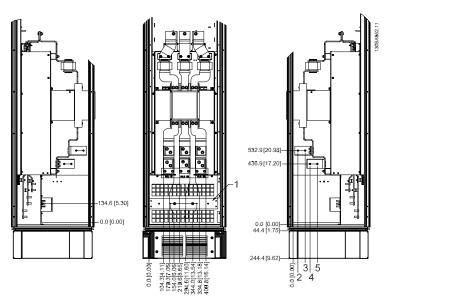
Posição do bloco de terminais - Cabine de Opcionais com disjuntor/ chave com cápsula moldada (Vistas esquerda, frontal e direita) A placa da glande esta 42 mm abaixo do nível .0.
